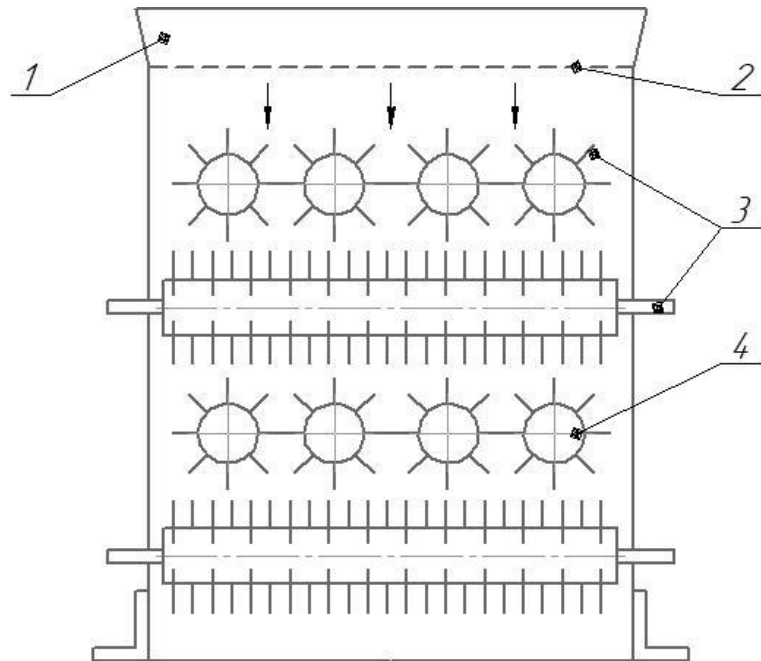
Конструктивна схема портального багатороторного змішувача безперервної дії
